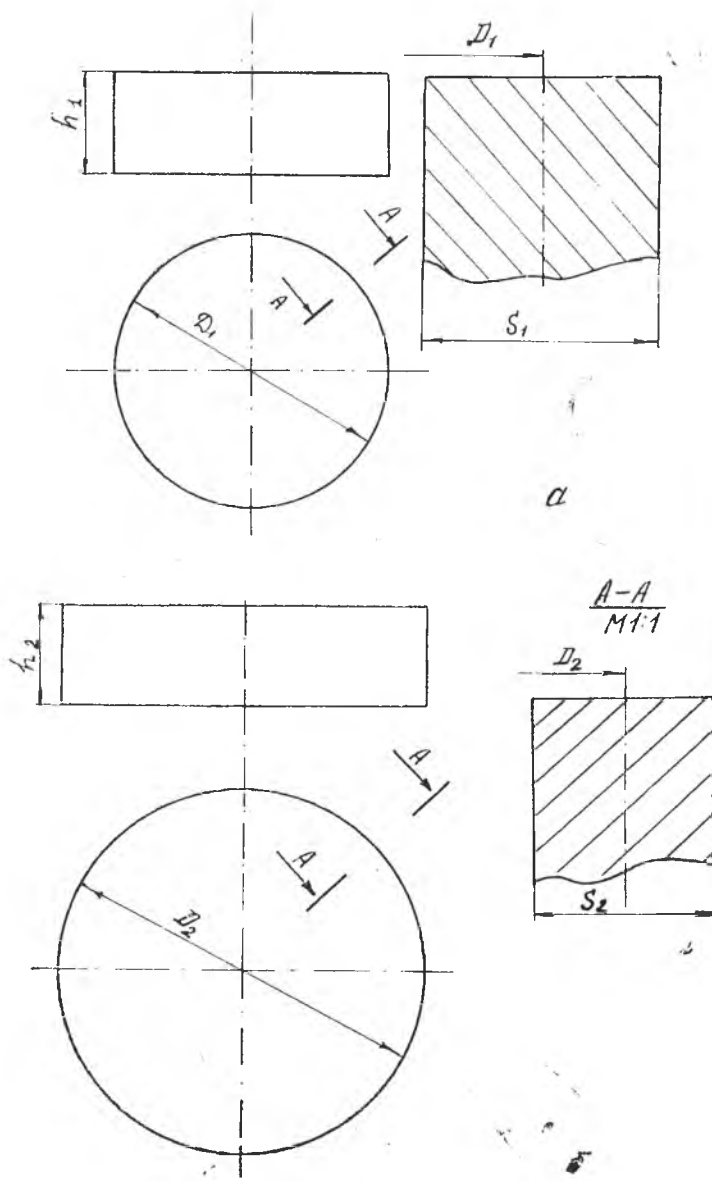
Схемы определения размеров исходной заготовки и готовой цилиндрической обечайки
